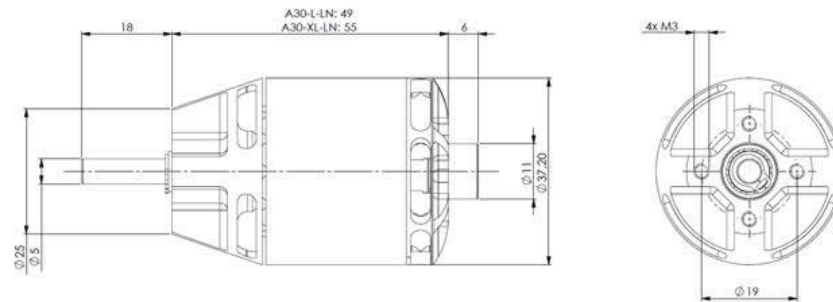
креслення двигуна Hacker Motor A30-10 XL-LN
